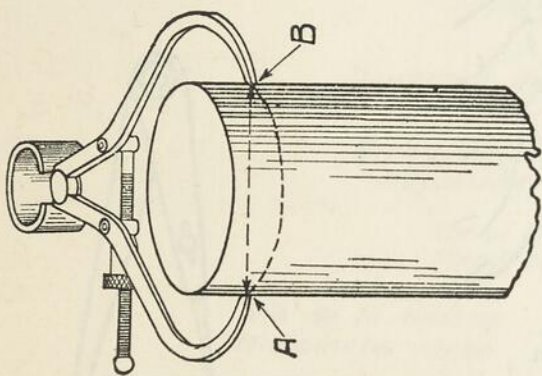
Calibrage au compas extérieur (South Bend Lathe Works)      Fig. 234. — Réglage du compas intérieur (South Bend Lathe Works)
